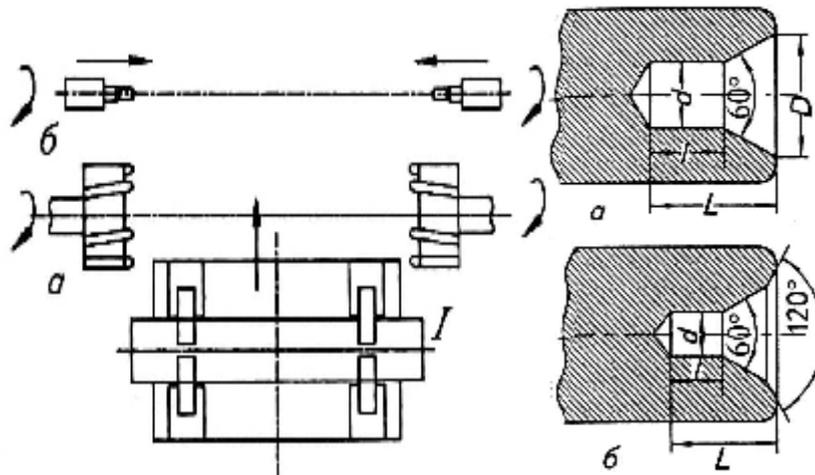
Схема организации торцевания и зацентровки заготовки и геометрия центровых отверстий с цилиндрическим отверстием под смазку
